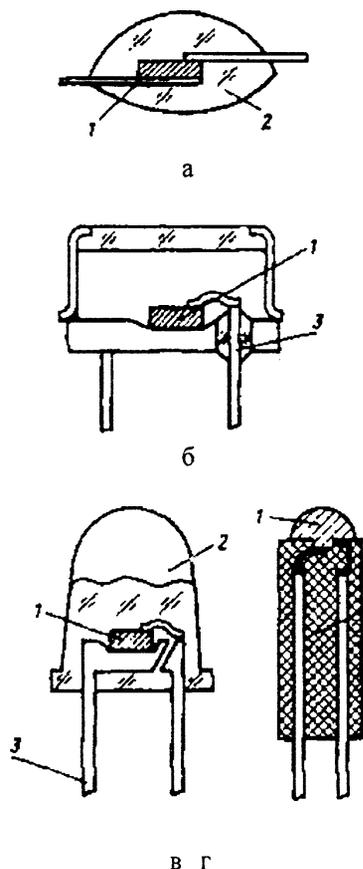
Конструкции некоторых типов СИД; а – бескорпусный; б – в металlostеклянном корпусе; в – с полимерной линзой в полимерном корпусе; 1 – кристалл; 2 – полимерная защита; 3 – ножка; 4 – полимерный корпус
